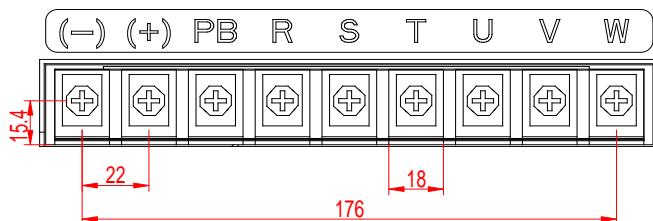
三相 380V 30~37kW 主回路端子 (单位: mm)
